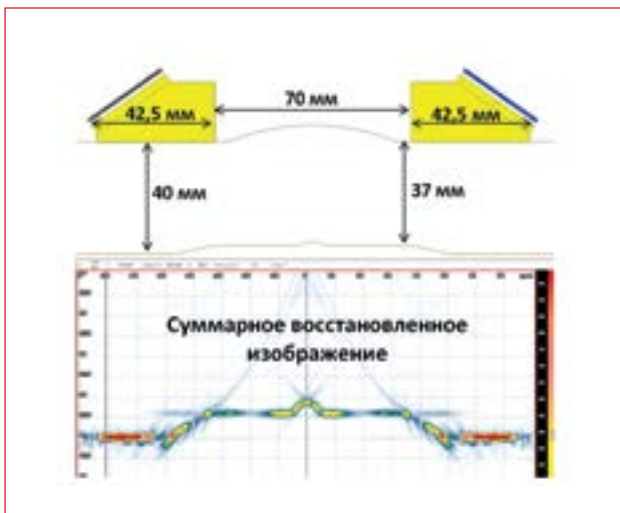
Профиль донной поверхности сварного соединения с вогнутым внутренним валиком
